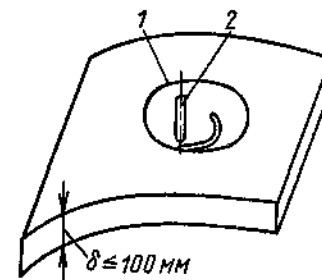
Пробивка начального отверстия в стали толщиной до 100 мм движущимся резаком при вырезке круглых отверстий под штуцера и патрубки:
